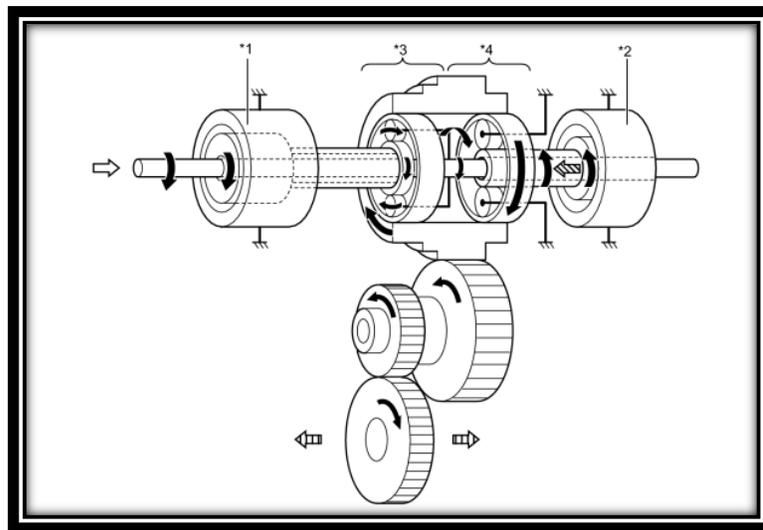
Fuerza Motriz de motor y trasmisión del MG2.
